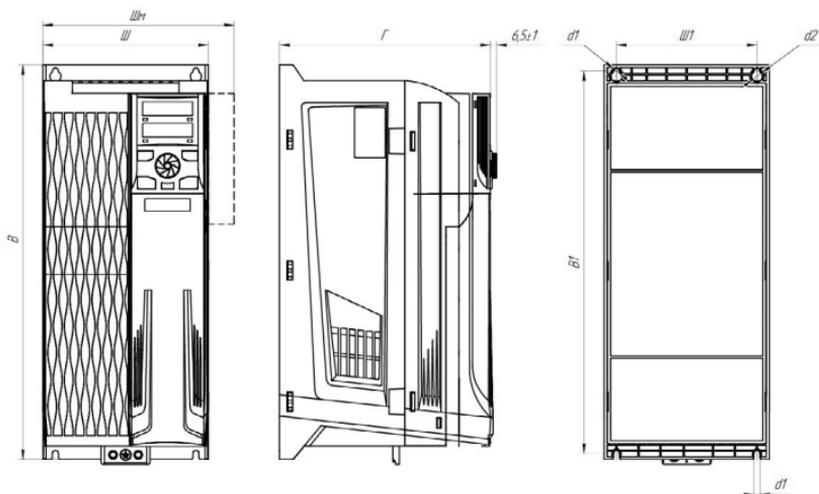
Габаритные и установочные размеры устройств серии INPRIME MX в пластмассовом корпусе (настенное исполнение), типоразмеры 1-4
